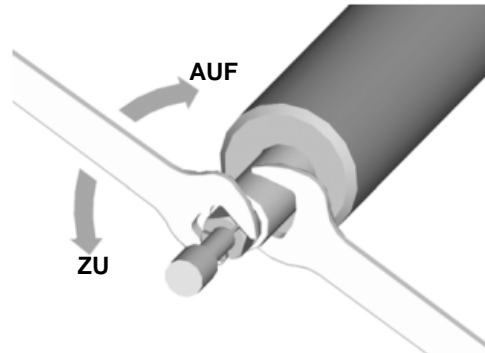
Werkzeugwechsel RL3040, RL 2732, RL 3622, RL 3030
